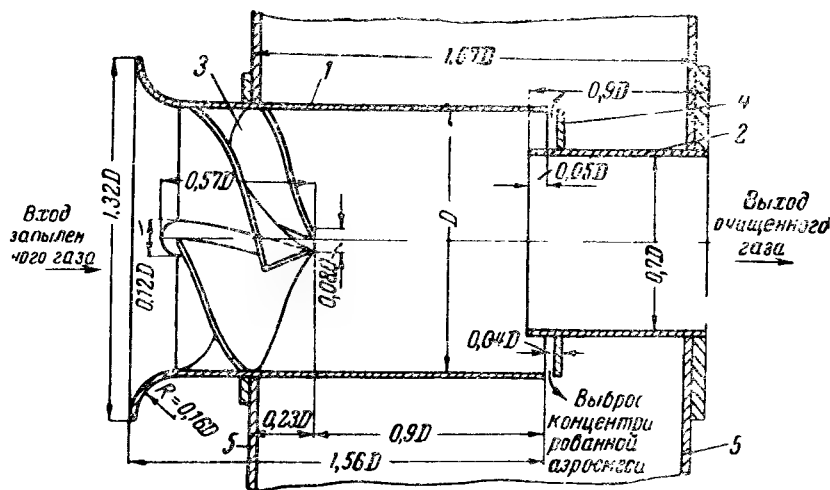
Горизонтальный прямооточный циклонный элемент. 1 — входная труба; 2 — выхлопная труба; 3 — розетка; 4 — шайба; 5 — корпус
